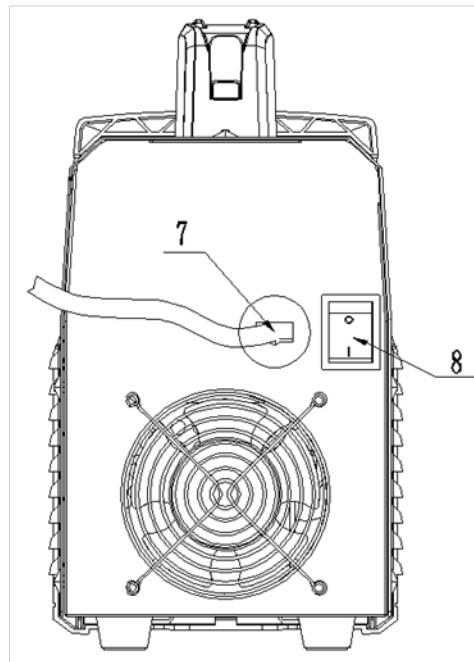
Общий вид (Инверторный сварочный аппарат постоянного тока MMA)
